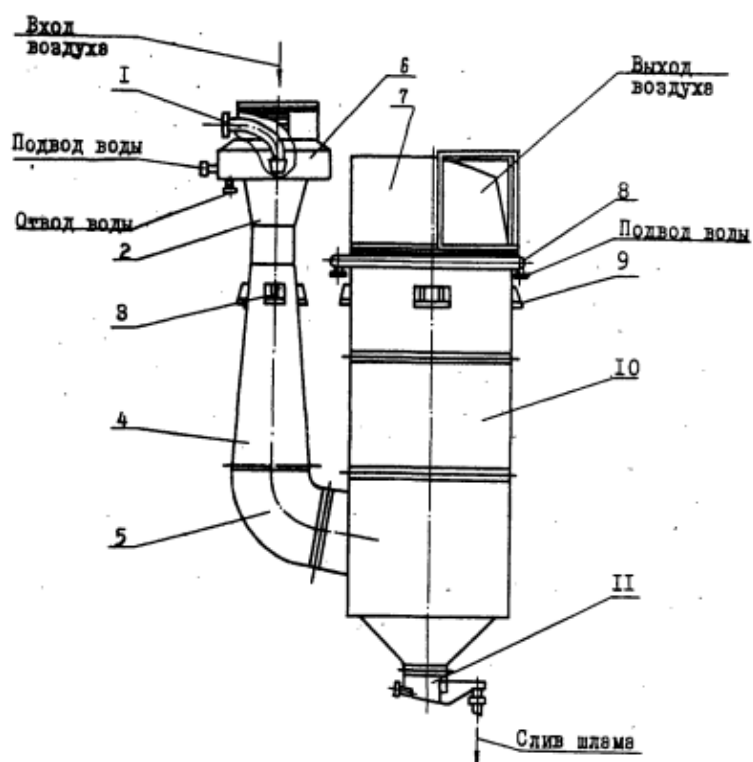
Пылеуловители типа КМП: 1 — форсунка с подводящей трубой; 2 — корпус трубы коагулятора; 3 — опора трубы коагулятора; 4 — труба-коагулятор; 5 — отвод соединительный с прямоугольным фланцем; 6 — водяная камера; 7 — улитка воздухоотводящая; 8 — установка сопел орошения стенок каплеуловителя; 9 — опора каплеуловителя; 10 — каплеуловитель; 11 — гидрозатвор 1
